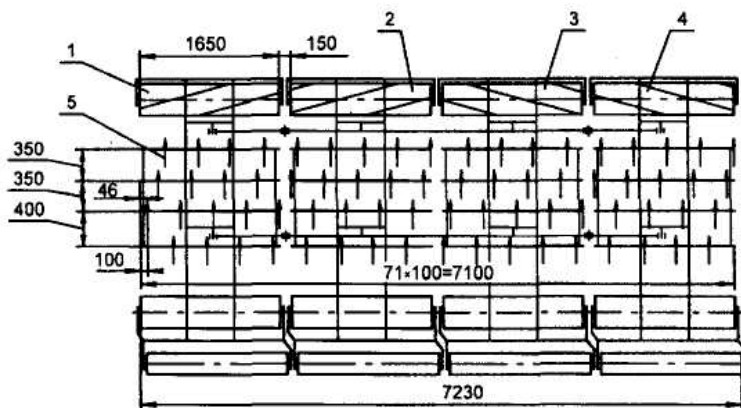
Схема расстановки рабочих органов агрегата АКШ-7,2:
